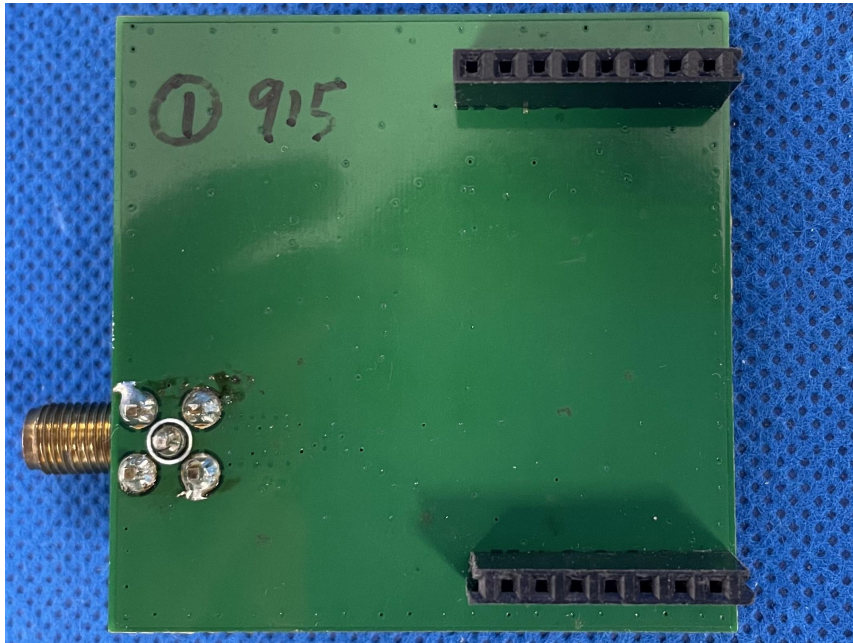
受试样机 ZM68S-C S0.00 焊接在 ZM1268S-T-PACK 后视图
